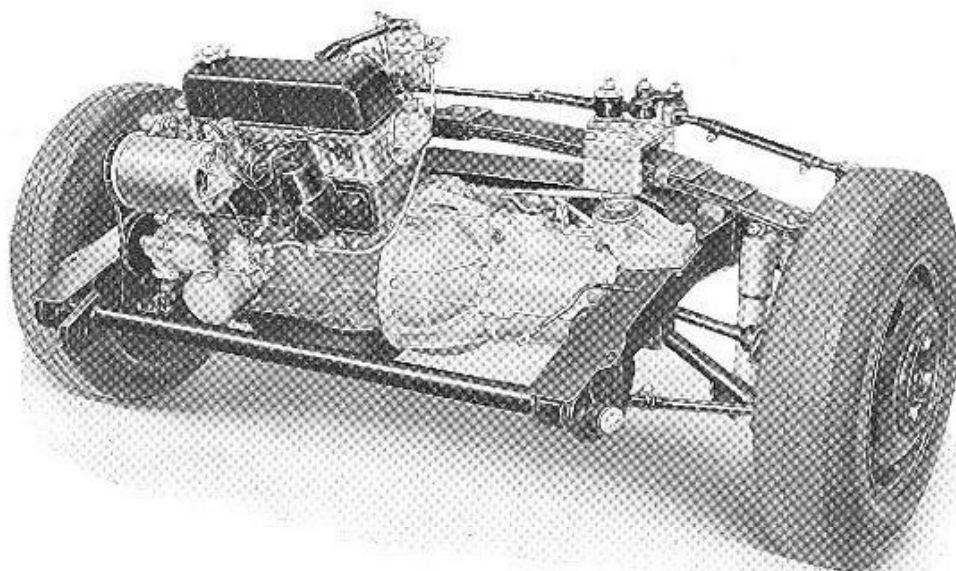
Linke Seitenansicht der Vorderrad- und Motoraufhängung.
